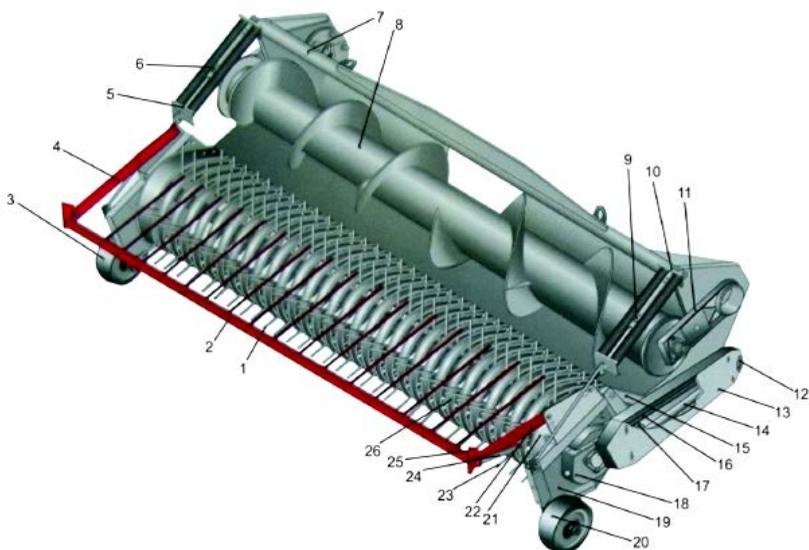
Платформа-подборщик комбайна «Дон-680М»: 1 – палец прижима; 2 – труба прижима; 3 – правое опорное колесо; 4 – стойка прижима; 5, 10 – правый и левый блок пружин разгружающего устройства; 6, 9 – пальцы установки в транспортное положение; 7 – каркас; 8 – шнек платформы; 11 – левый рычаг шнека; 12 – шкив с муфтой обратного хода; 13 – защитный щиток; 14 – распорка натяжения ремней; 15 – рычаг крепления; 16 – ремни привода; 17 – шкив привода; 18 – редуктор привода; 19 – левая боковина; 20 – левое опорное колесо; 21 – скат боковой левый; 22 – левая стойка прижима; 23 – зубья пружинные подбирающего устройства; 24 – пружина натяжения прижима; 25 – кронштейн упора трубы прижима; 26 – скат подборщика
